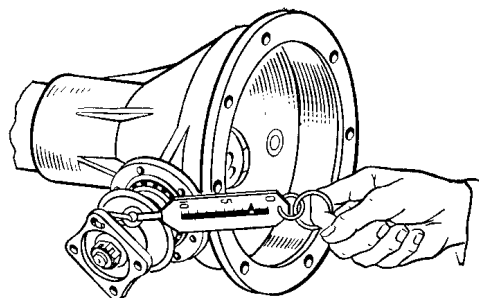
Проверка затяжки подшипников вала ведущей шестерни
